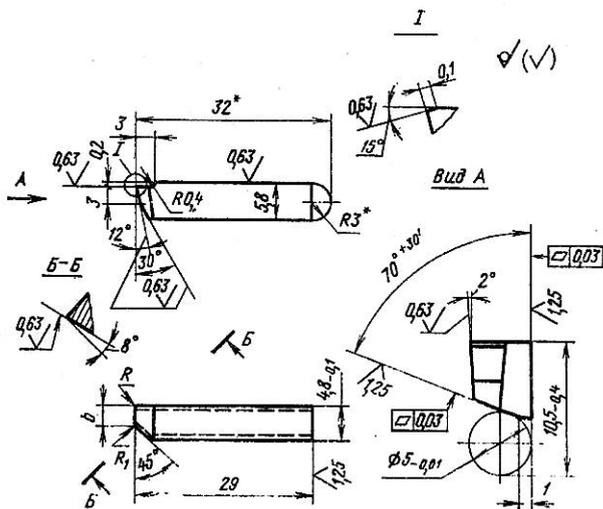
Резец для проточки наружных резьбовых канавок П39.08Л.000:
